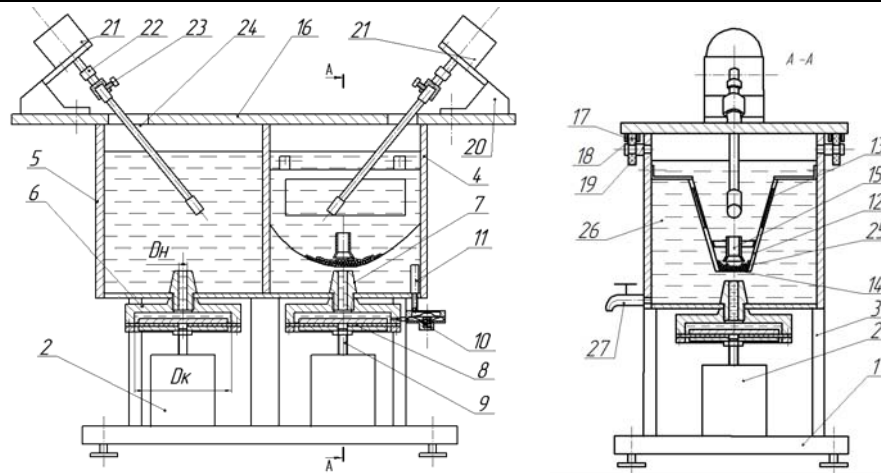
Конструкція вібраційної машини для очистки забруднень потоком твердих часток та мийки деталей при ремонті обладнання: 1 - основа; 2 - вібропривід; 3 - стійкі; 4 - ванна; 5 - полістиролові кульки; 6 - корпус камери пульсації; 7 - насадок (діаметром D_H); 8 - мембрана з дисками; 9 - шток; 10 - мембранний клапан; 11 - забірня трубка; 12 - контейнер; 13 - бокові сітки; 14 - сітка; 15 - сопло; 16 - кришка; 17 - напрямні; 18 - ролики; 19 - осі; 20 - кутник; 21 - мотор-редуктор; 22 - муфта; 23 - затискач; 24 - деталь; 25 - тверді частки (полістиролові кульки); 26 - миюча рідина; 27 - кран для зливу
